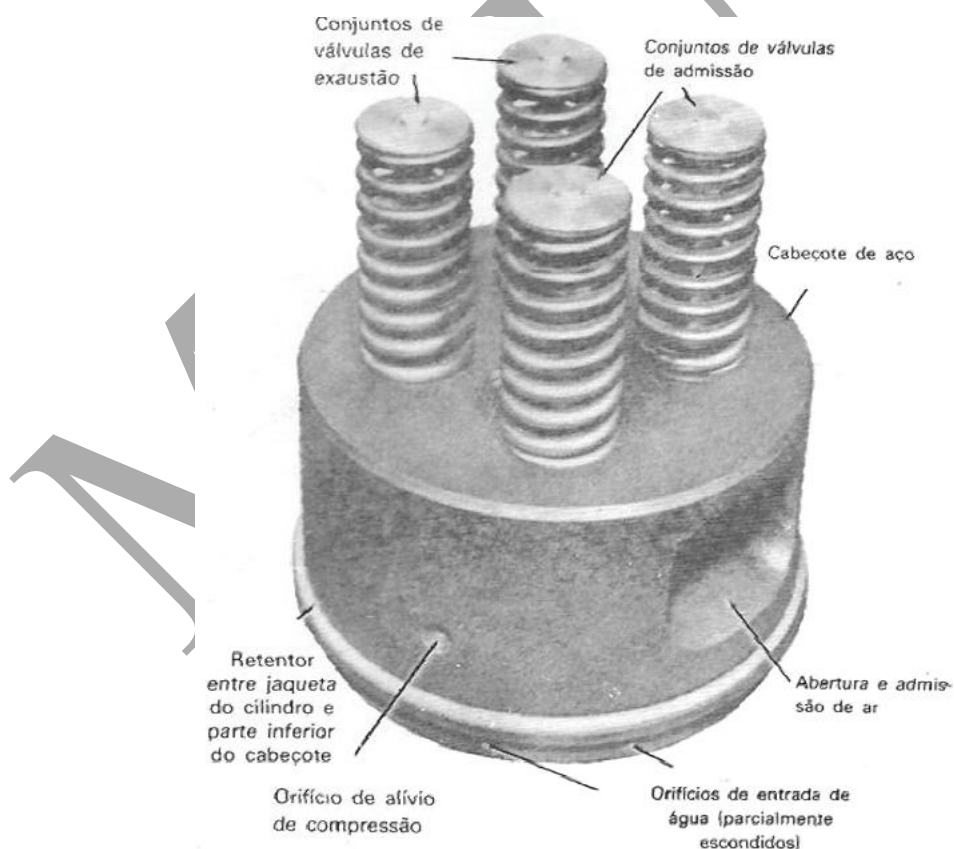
Conjuntos de força do motor diesel conjugado (soldado) e separado.
